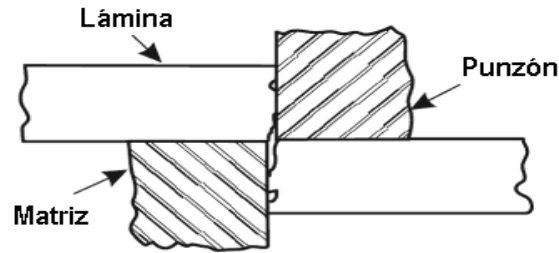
Un claro insuficiente resulta en una doble fractura
